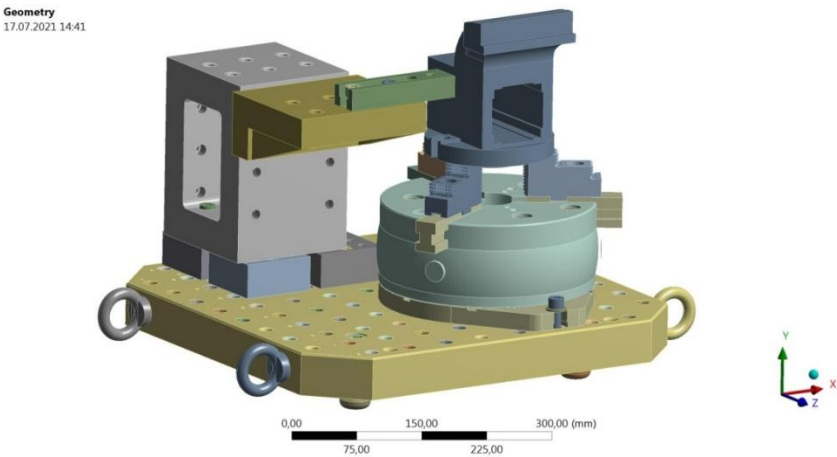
Геометрическая 3D-модель приспособления в сборе с обрабатываемой заготовкой в расчетной среде ANSYS®Mechanical
